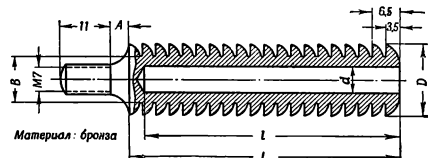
Различные конструкции вишеров для чистки канала ствола дробового ружья:
